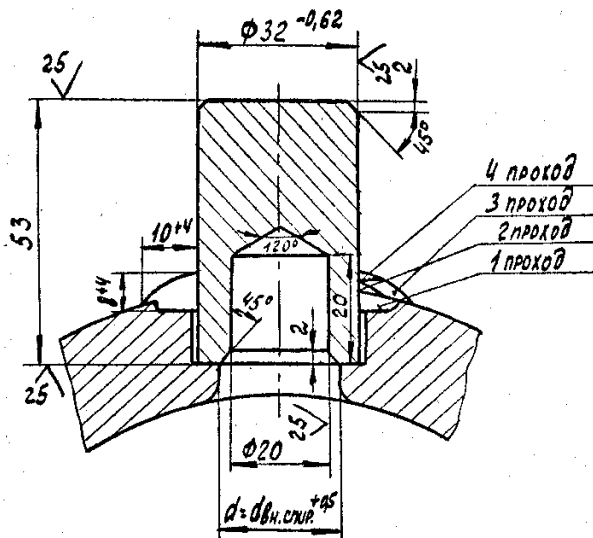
Подготовка отверстий под приварку спиралей
